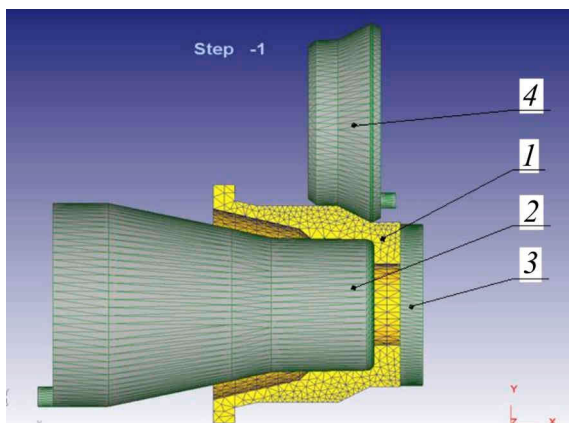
Схема раскатки: 1 – заготовка, 2 – оправка, 3 – прижим, 4 – ролик
